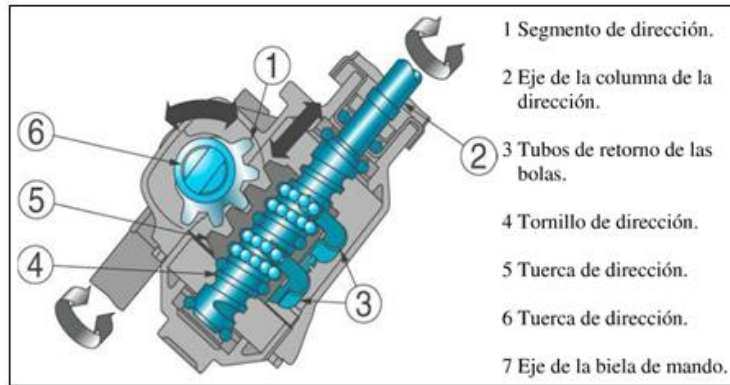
Mecanismo de dirección por tornillos sinfín cilíndrico y bolas recirculantes
